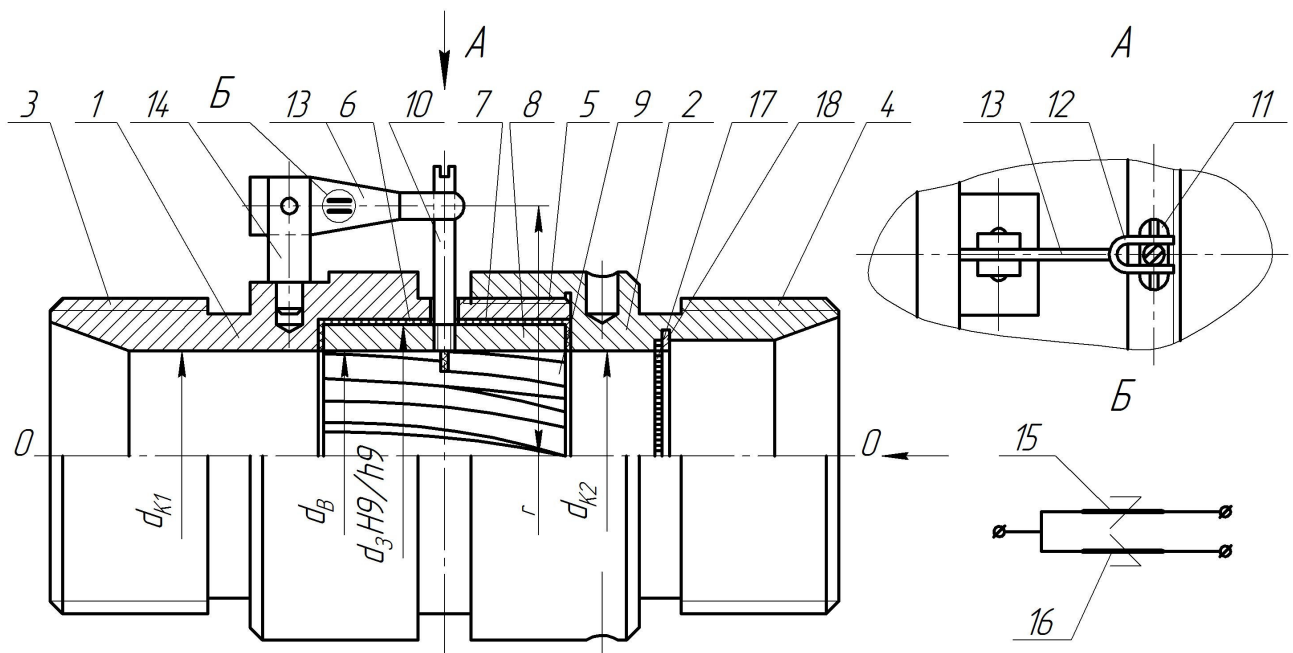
Прилад для вимірювання витрати моторного палива
